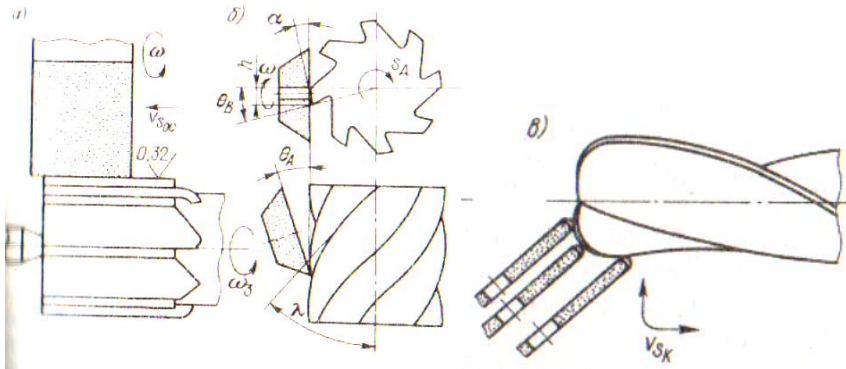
Схемы заточки задней поверхности многолезвийного инструмента с прямыми зубьями-а; с винтовыми зубьями - б; радиусного инструмента – в; (h - смещение круга; Θ_A и Θ_B – углы разворота шлифовальной головки)
